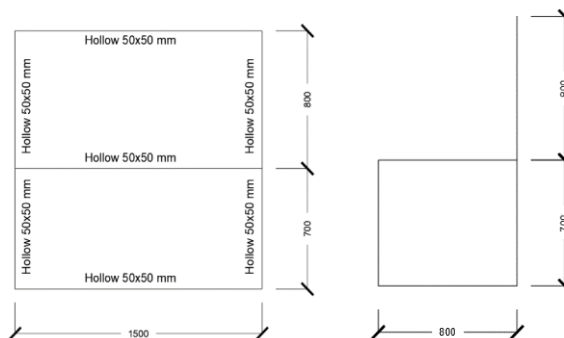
, dan gambar tampak depan serta tampak samping keranjang repair dapat dilihat pada Gambar 6.8.
